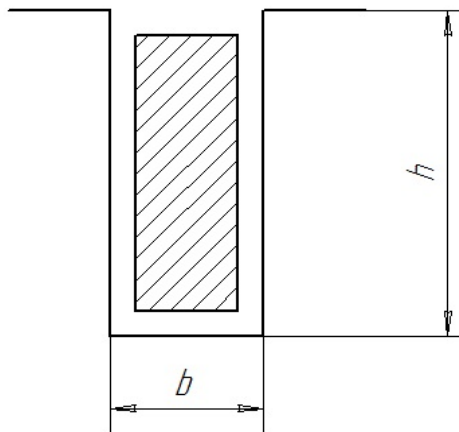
Паз и стержень обмотки глубокопазного ротора
